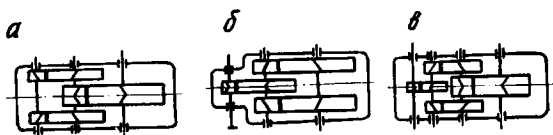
Схемы редукторов с раздвоенными ступенями:
